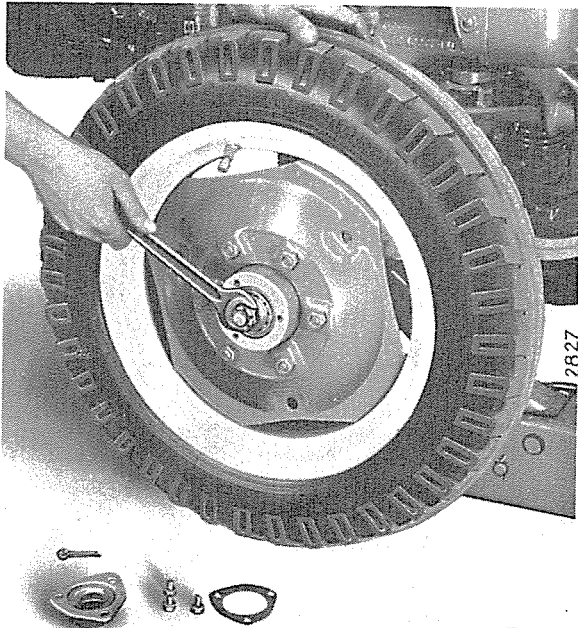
Dépose du couvercle du moyeu et de son joint.
